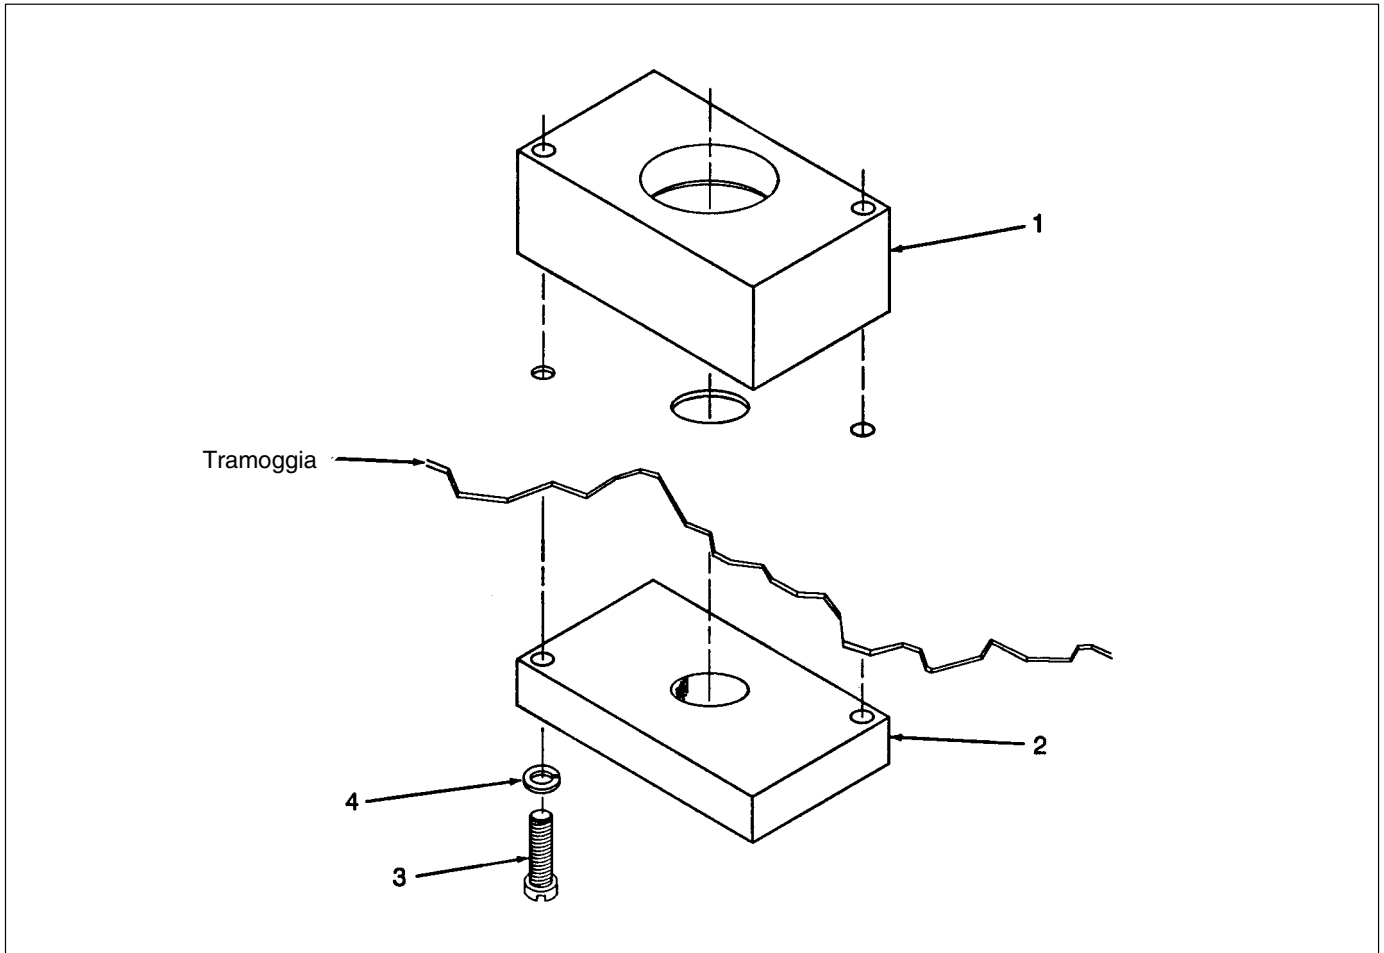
Disegno esploso kit di montaggio pompa singola
